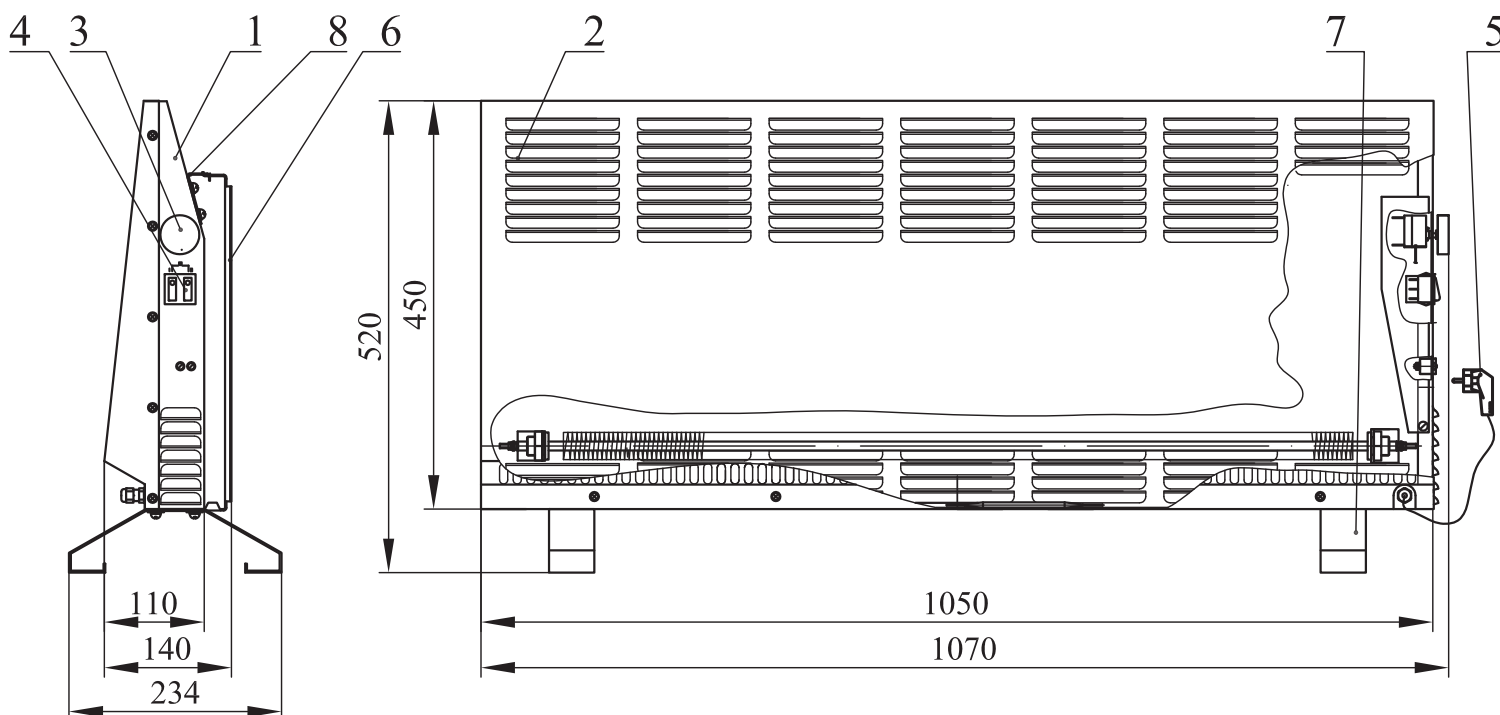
1 - Корпус, 2 - Крышка, 3 - Ручка термостата, 4 - Клавишный выключатель, 5 - Шнур с вилкой, 6 - Кронштейн настенный (для настенной установки - 2 шт.), 7 - Ножка (для напольной установки - 2 шт.), 8 - Ручка для перемещения конвектора (2 шт.)
